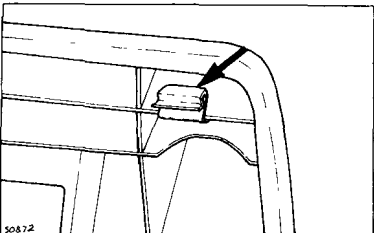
Защелка верхней панели приборного щитка — Renault 11
